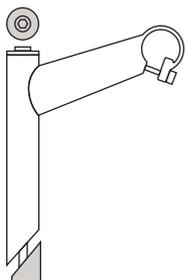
Конструкция резьбовой рулевой колонки и регулировка положения руля
